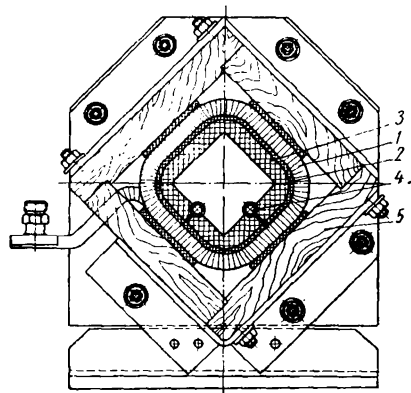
Индуктор для нагрева квадратных заготовок: 1 — обмотка; 2 — изолирующая гильза; 3 — шамотные кирпичики; 4 — немагнитные металлические направляющие; 5 — деревянный предохранительный короб
